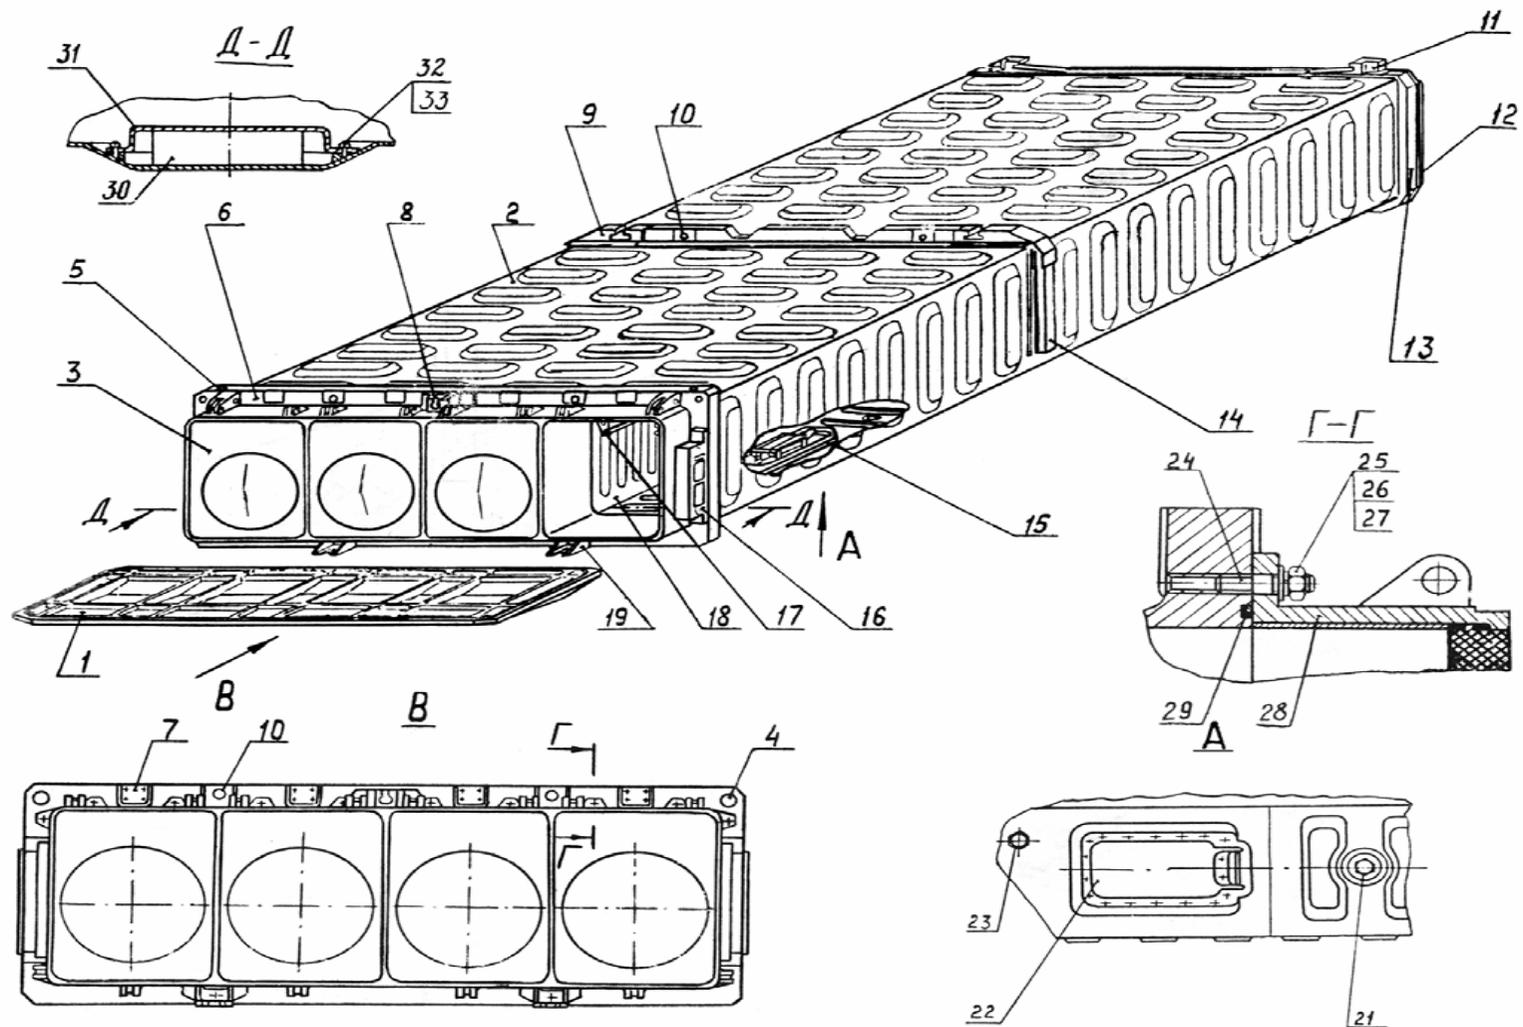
Транспортно-пусковой контейнер: 1 – крышка передняя; 2 – корпус; 3 – крышка разрушающаяся; 4 – отверстие; 5 – гнездо; 6 – шпангоут передний; 7 – пластина; 8,19 – кронштейн; 9 – бугель передний; 10 – узел подъема; 11 – бугель задний; 12 – крышка задняя; 13 – шпангоут задний; 14 – шпангоут средний; 15 – механизм расстыковки электроразъема; 16 – электроразъем; 17 – балка направляющая; 18 – диафрагма; 20,23 – пробка для продувки; 21 – пробка люка переключения литеры; 22 – крышка механизма расстыковки электроразъема; 24 – шпилька; 25 – гайка; 26,27,33 – шайба; 28 – ЗГУРД; 29 – прокладка; 30 – осушитель (силикагель); 31 – крышка; 32 – винт
